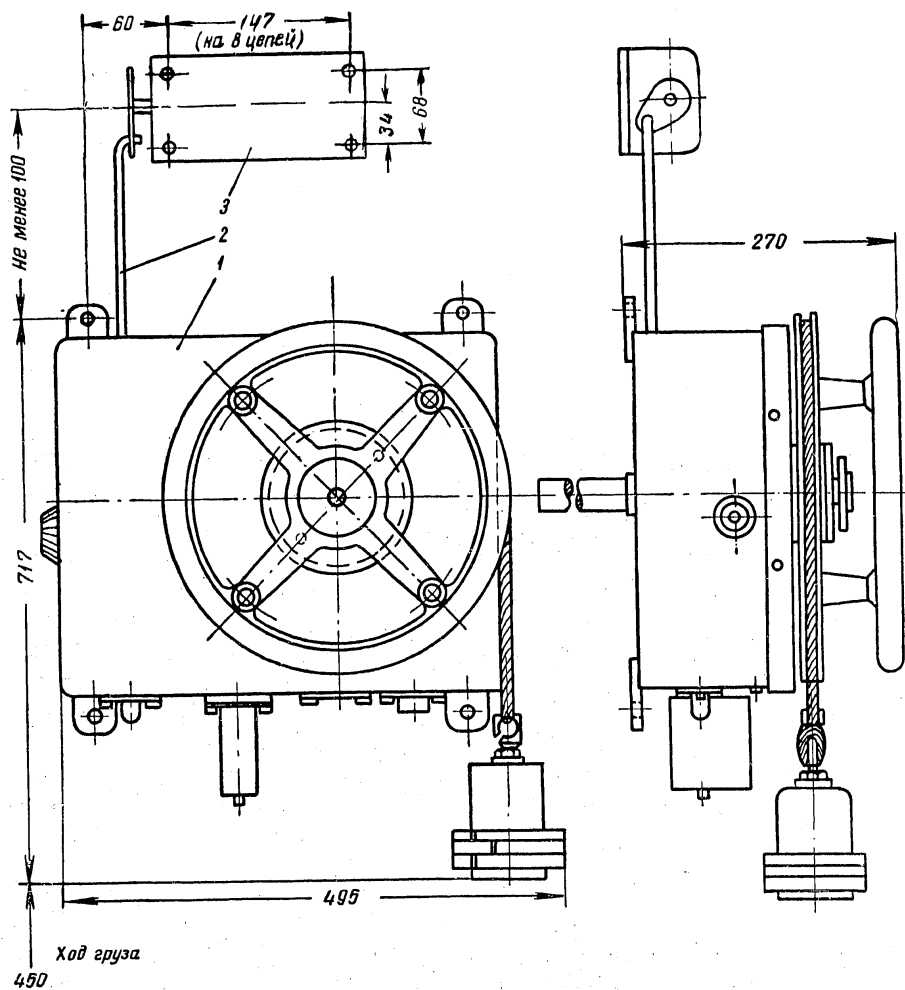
Установка блокконтактов КСА к грузовому приводу типа ПГ-10 для выключателей:
